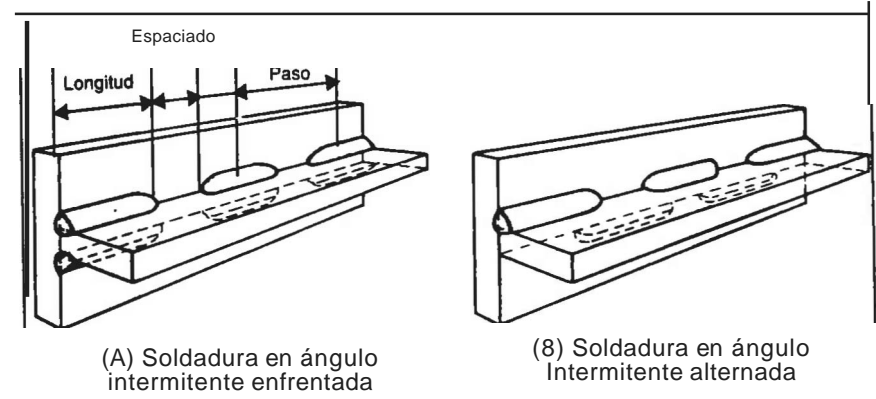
SOLDADURAS EN ÁNGULO INTERMITENTES
